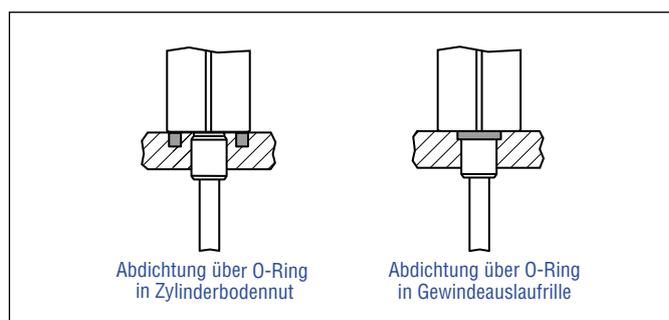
Möglichkeiten der Abdichtung für Gewindeflansch mit flacher Flanschfläche
